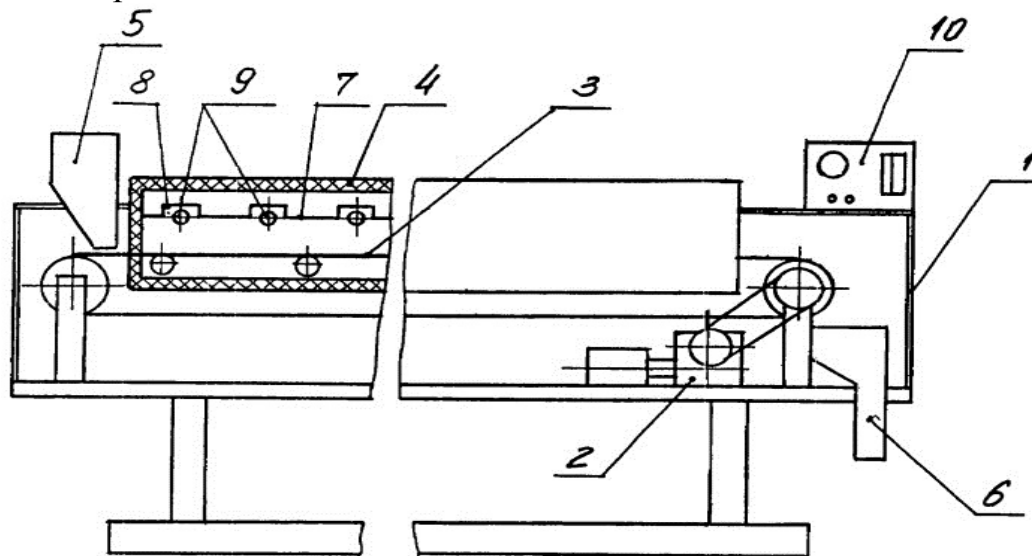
Схема установки для термообработки насыпного пищевого материала (1-мотор-редуктор; 2- частотное регулирование скорости движения конвейерной ленты; 3- конвейерная лента; 4-нагревательный блок; 5-дозировующий бункер; 6-отводящий лоток; 7-плоская панель; 8-туннели; 9-инфракрасные излучатели).
